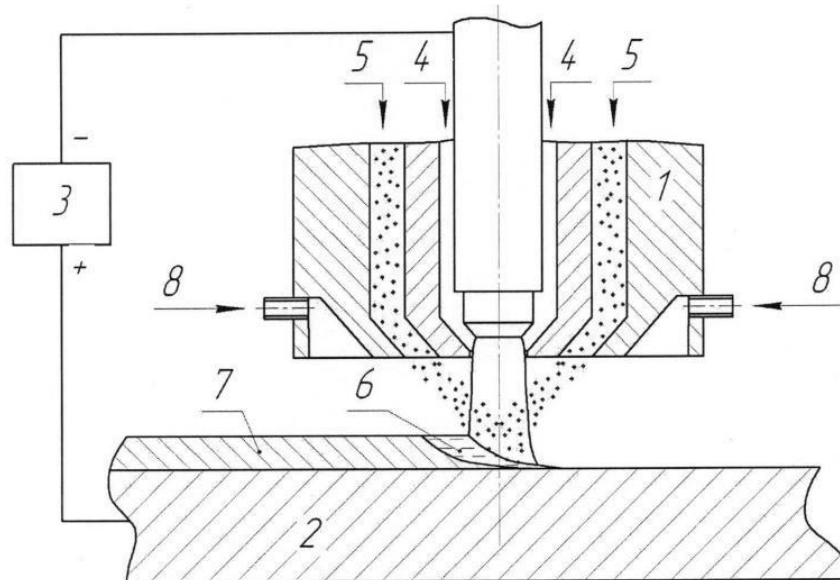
Схема плазово-порошкового наплавлення: 1 – плазмотрон; 2 – деталь; 3 – джерело живлення; 4 – канал для транспортуючого газу; 5 – канал для подачі порошку; 6 – зона оплавлення; 7 – наплавлений шар; 8 – канал для подачі охолоджувальної рідини [2].
